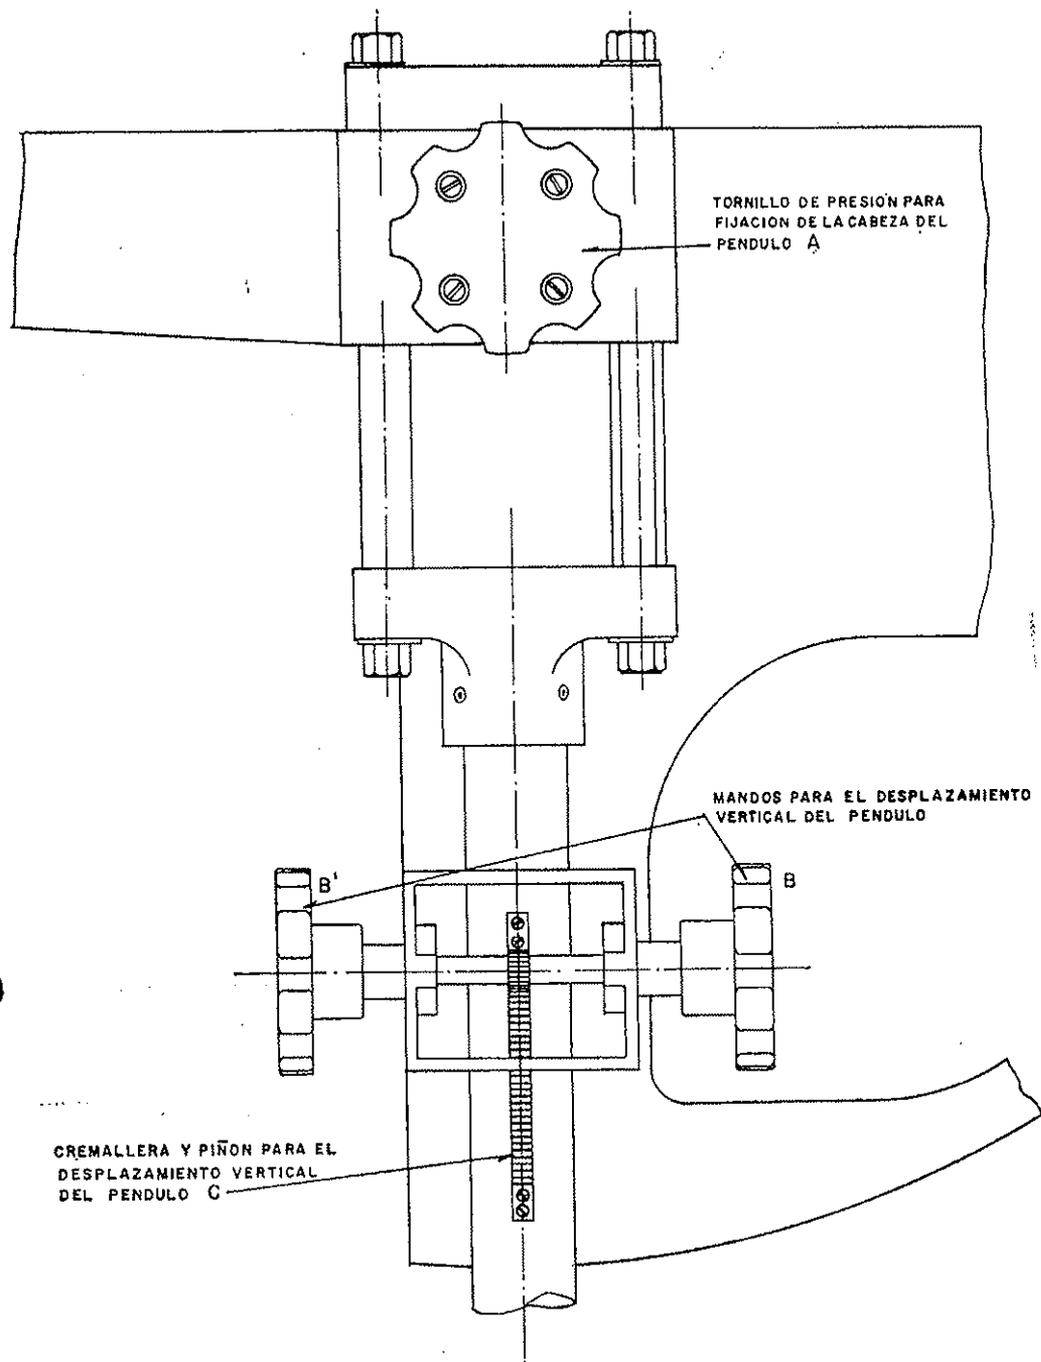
Detalle del dispositivo de desplazamiento vertical del péndulo.
